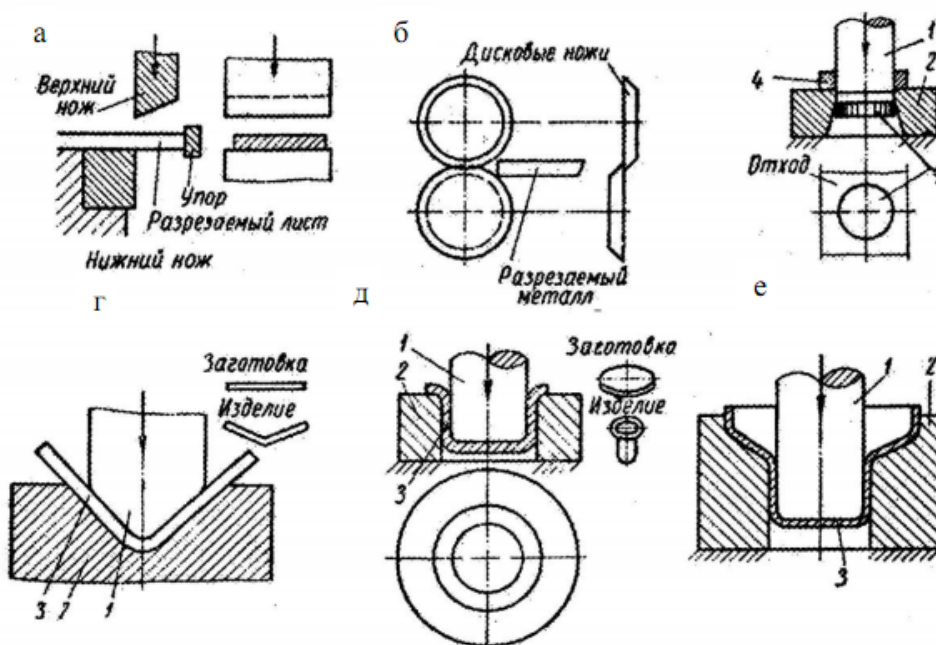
Операции листовой штамповки: 1 – пуансоны; 2 – матрица; 3 – изделие; 4 – отход
